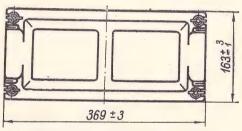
Габаритный чертеж аккумуляторной батареи 12-CAM-28
